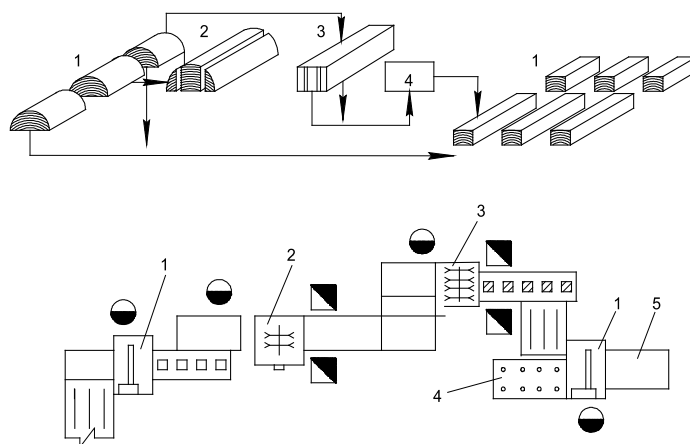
Узел переработки горбылей на базе обрезного и многопильного станков. 1 – торцовочный станок; 2, 3 – многопильные станки; 4 – узел нанесения насечек на поверхность досок; 5 – узел сборки каркаса
